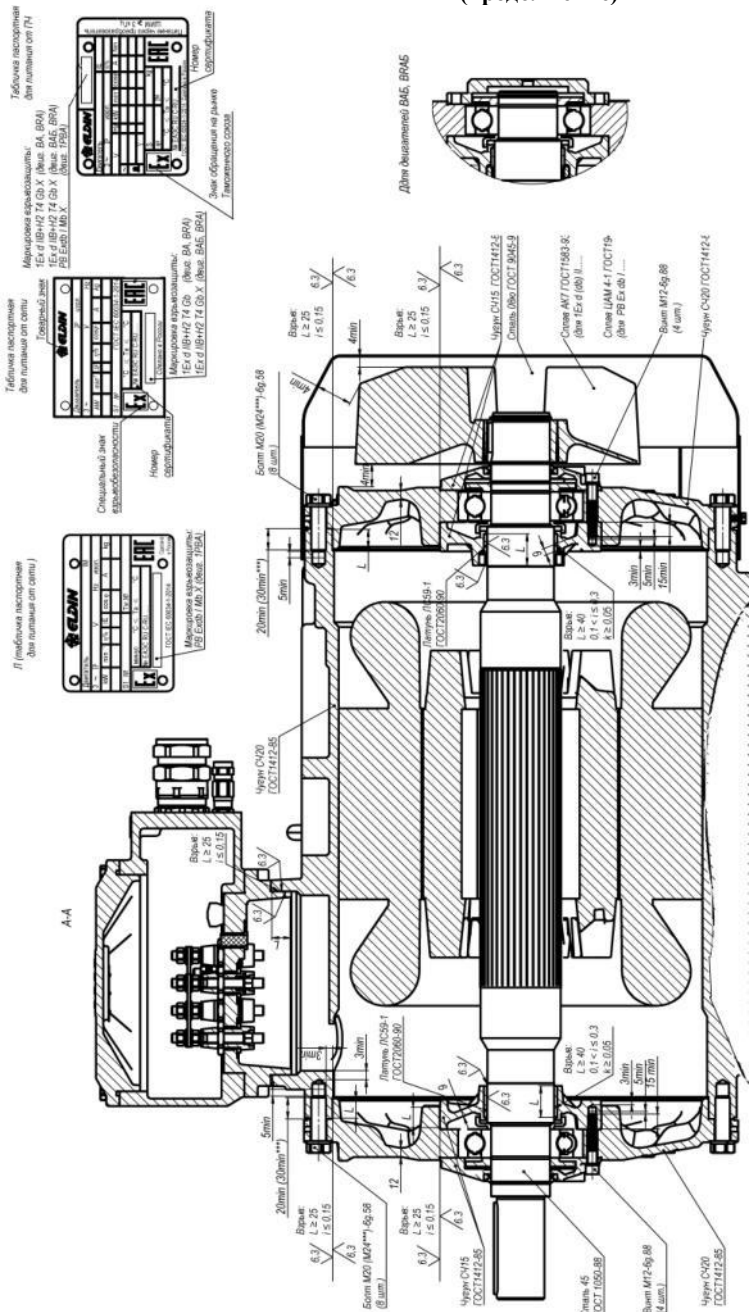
Чертеж взрывозащиты коробки выводов «д» двигателей ВА(Б),1РВА 250,280; ВРА(Б),1РВРА 280,315
